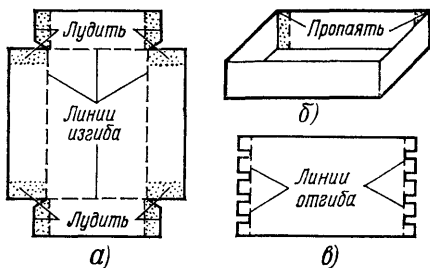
Изготовление корпуса прибора: а — заготовка (развертка) корпуса; б — корпус после гибки заготовки и пропайки стыков; в — заготовка (развертка) поддона
